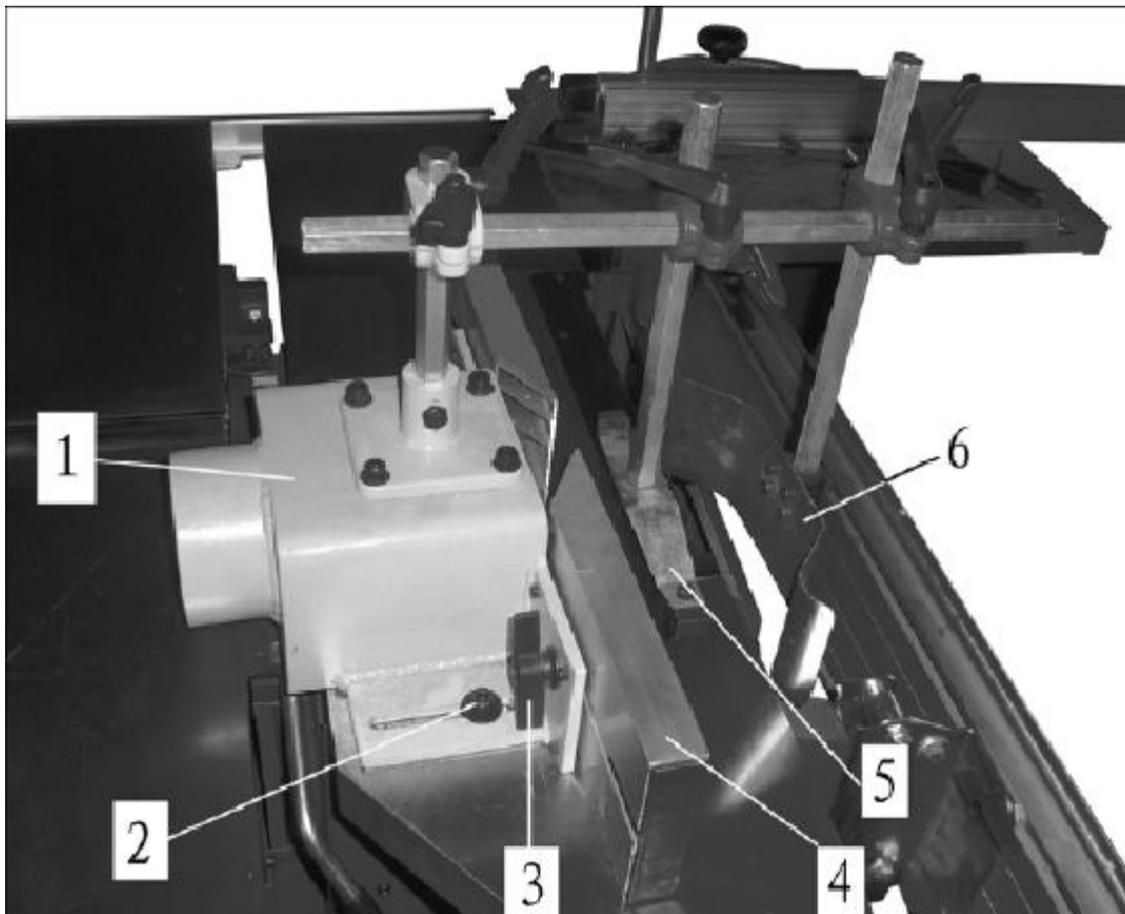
Станок комбинированный деревообрабатывающий модели CWM-250-5/230
